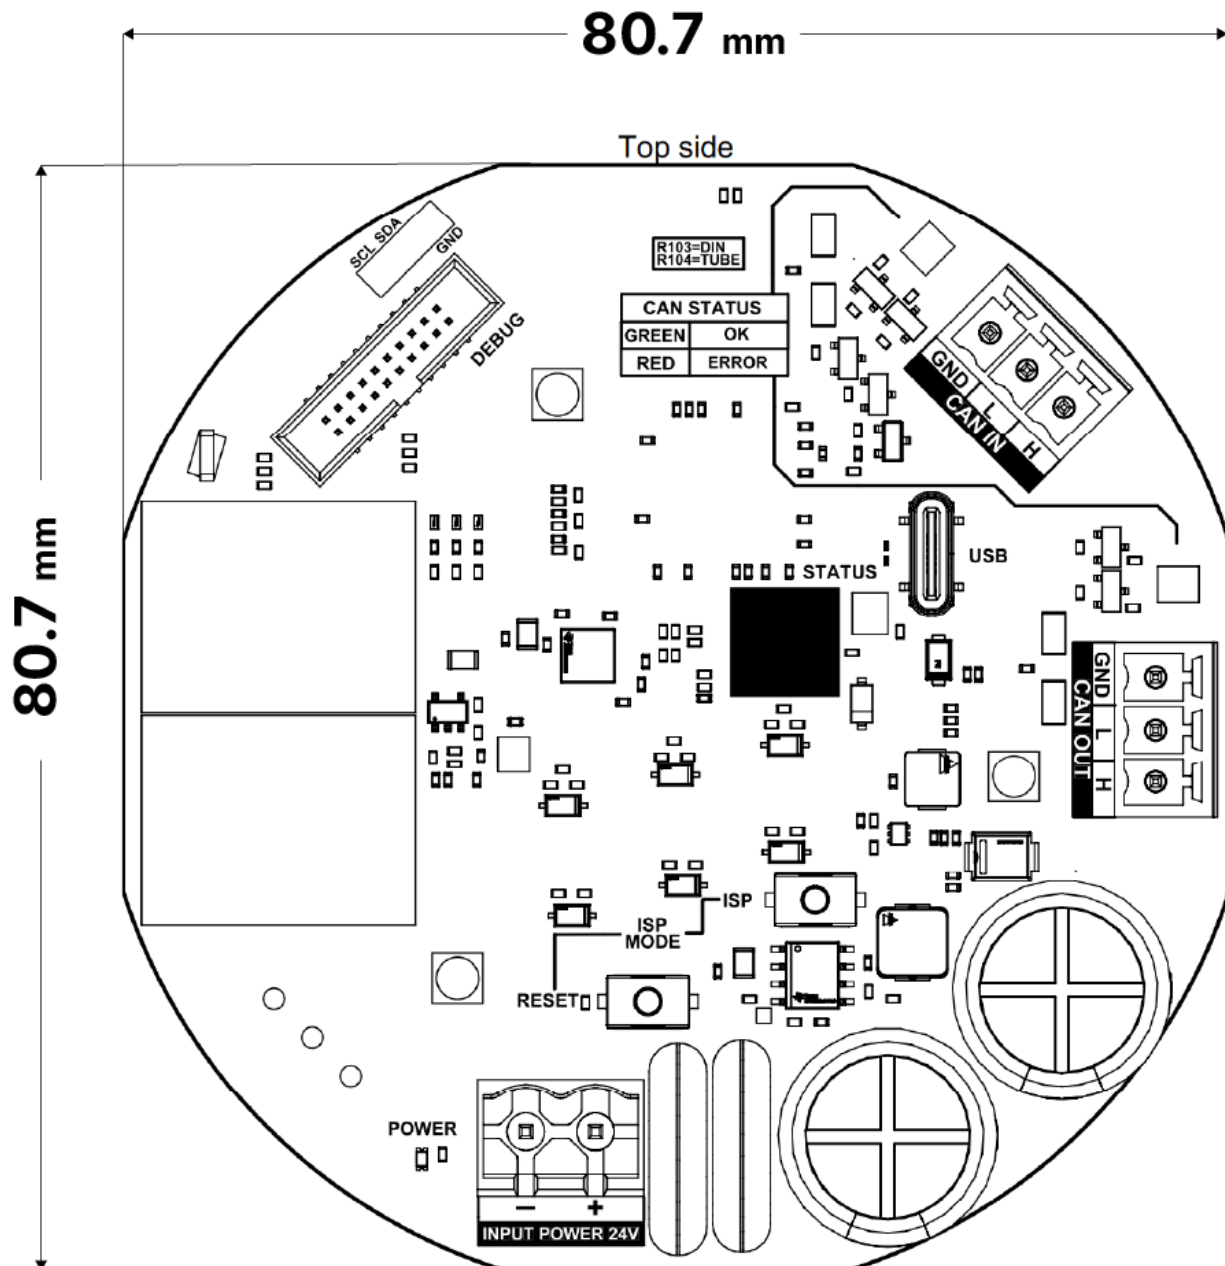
Abmessungen des Erweiterungsmoduls BLDC TUBE
